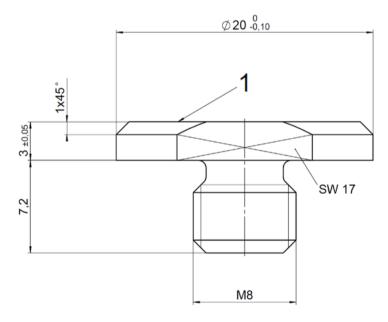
P-176.F35 (1 = Fläche gehärtet und poliert)
